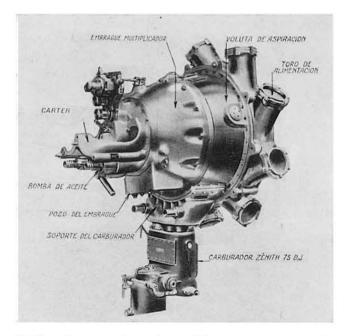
Compresor de mando mecánico para motor en estrella Siemens & Halske de 420 cv.
